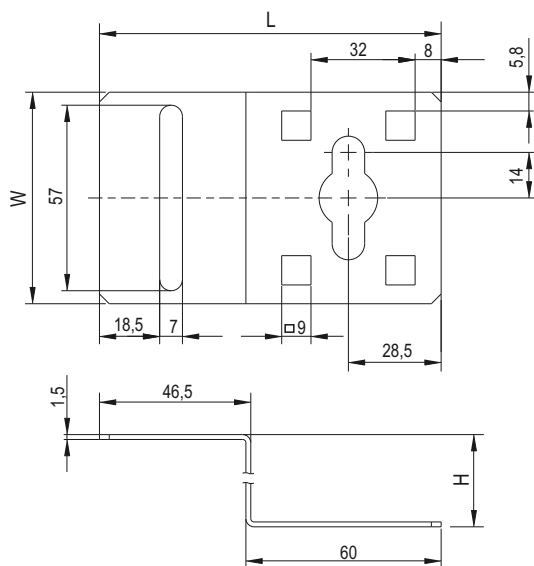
Кронштейн крепления между профилем и боковой стенкой / Figure 4 – Mounting bracket between the profile and the side wall / 4-сурет – Профиль мен бүйір қабырғаның арасын бекіту кронштейні (ITK-HP-20)
